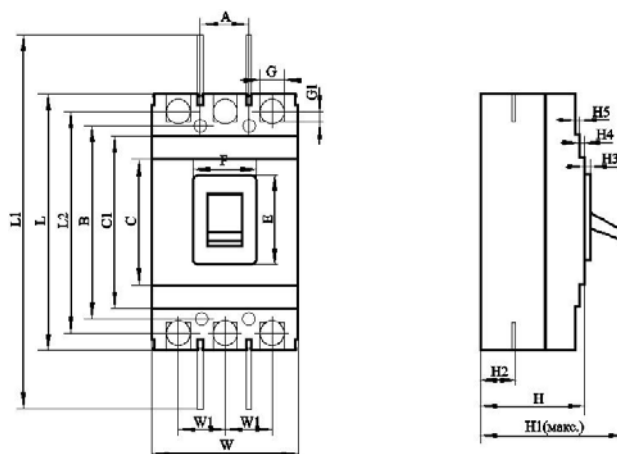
Габаритные и установочные размеры выключателей BA77-400, BA77-630, BA77-800, BA77-1250.
